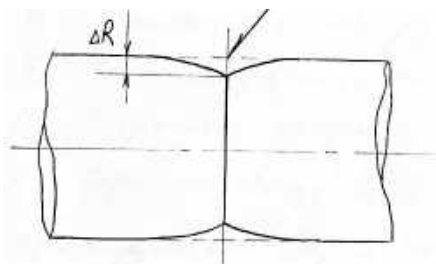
Деформування труби від зварювання стикового шва
